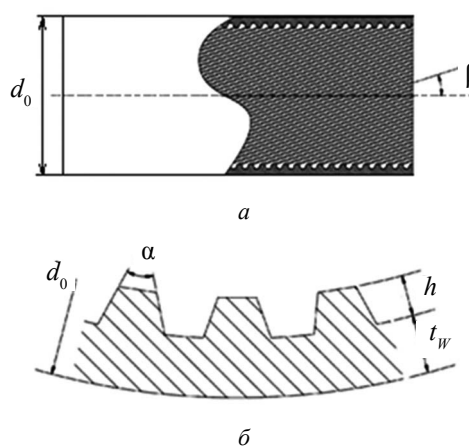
Схема трубы: а — продольное сечение; б — поперечный разрез
